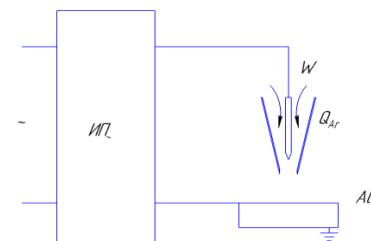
Схема сварочного поста при сварке сжатой дугой
